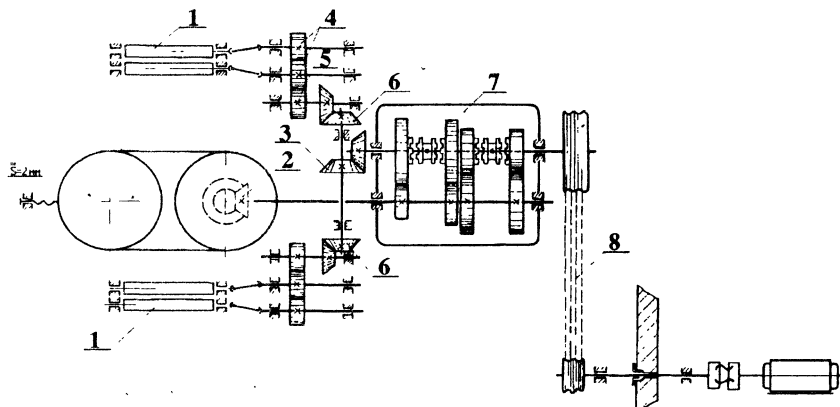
Ленточный резательный станок. Кинематическая схема.
